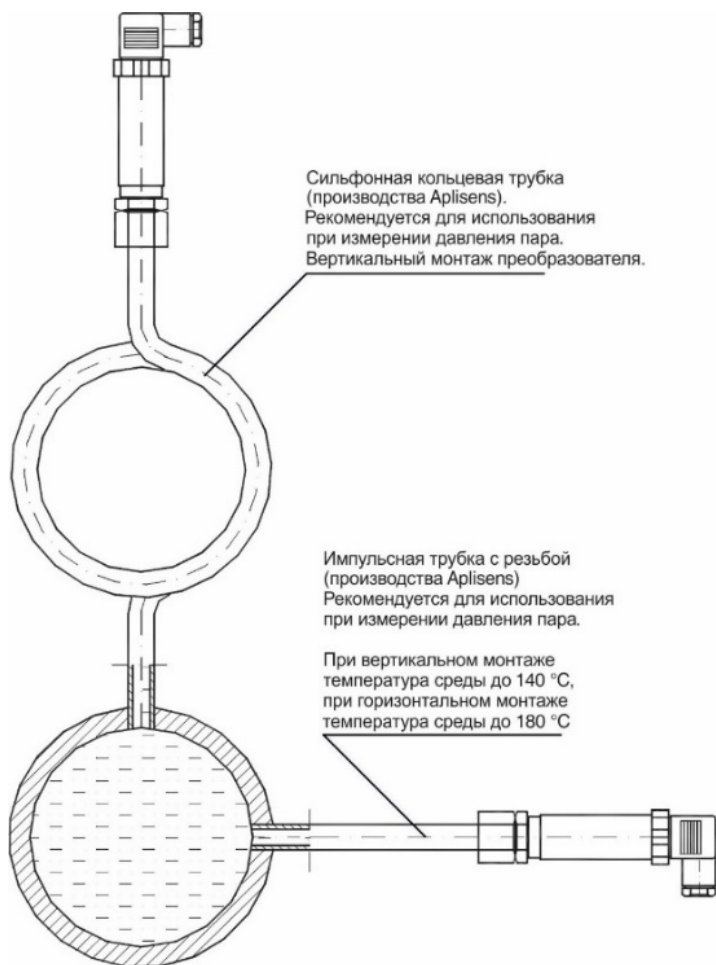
Способ крепления преобразователя PR-28 с присоединением типа С.
